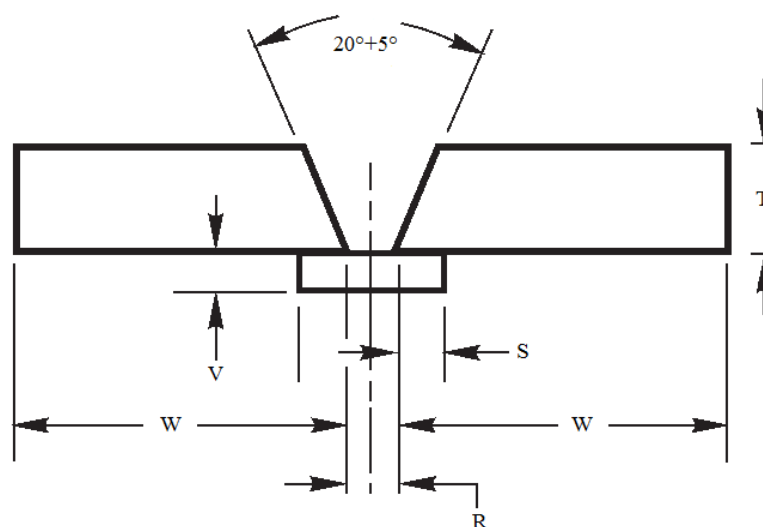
Montaje de la probeta de soldadura con ranura [41].
